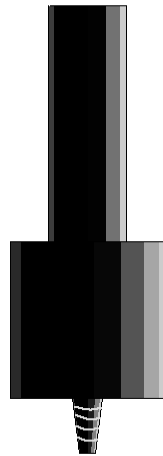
Herramienta diseñada en Mechanical Desktop con la forma de pin triflute
